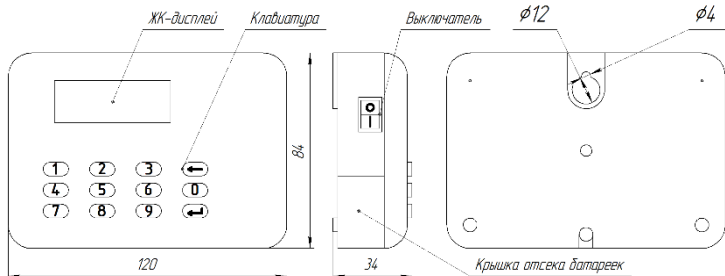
Размеры и основные элементы индикаторного устройства
